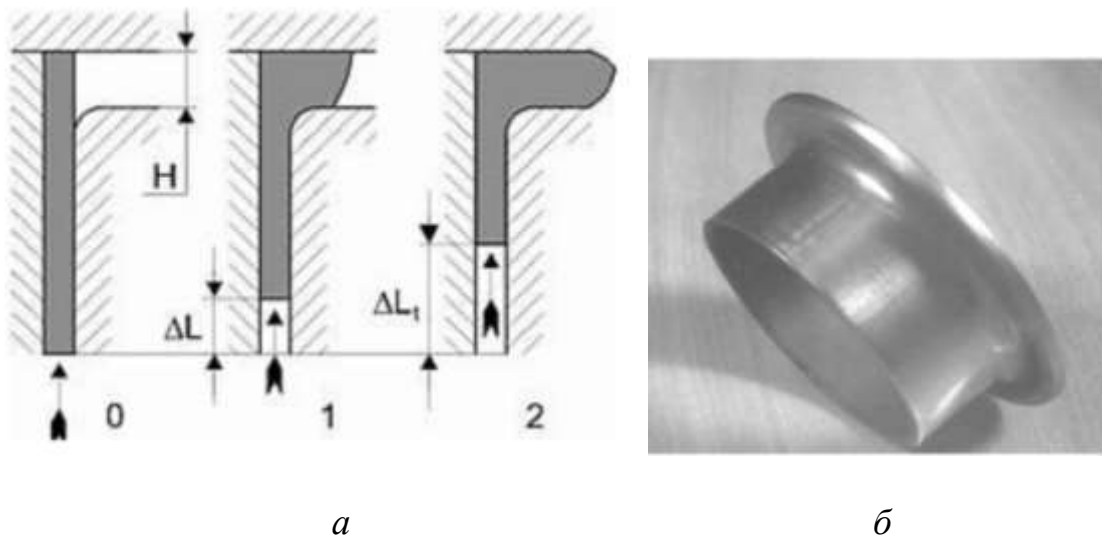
Схема торцевої розкатки комбінованої з радіальним видавлюванням (а) для виготовлення деталей з потовщеним фланцем (б)
